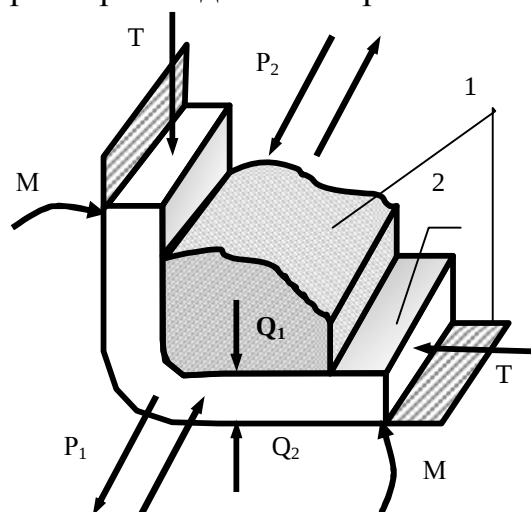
Схемы приложения сил к заготовке: 1 – формующий инструмент; 2 – заготовка
